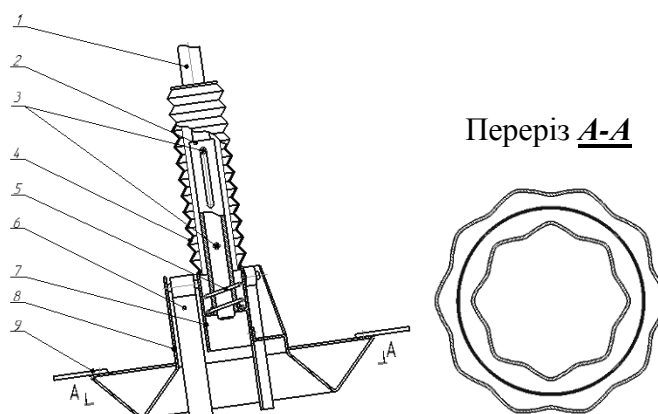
Пристрій для одночасного зрізування гички та очищення головок коренеплодів цукрових буряків [6]: 1 – вал, 2 – втулка, 3 – штифт, 4 – кожух, 5 – пружина, 6 – еластична лопать, 7 – маточина, 8 – диск, 9 – ніж.
